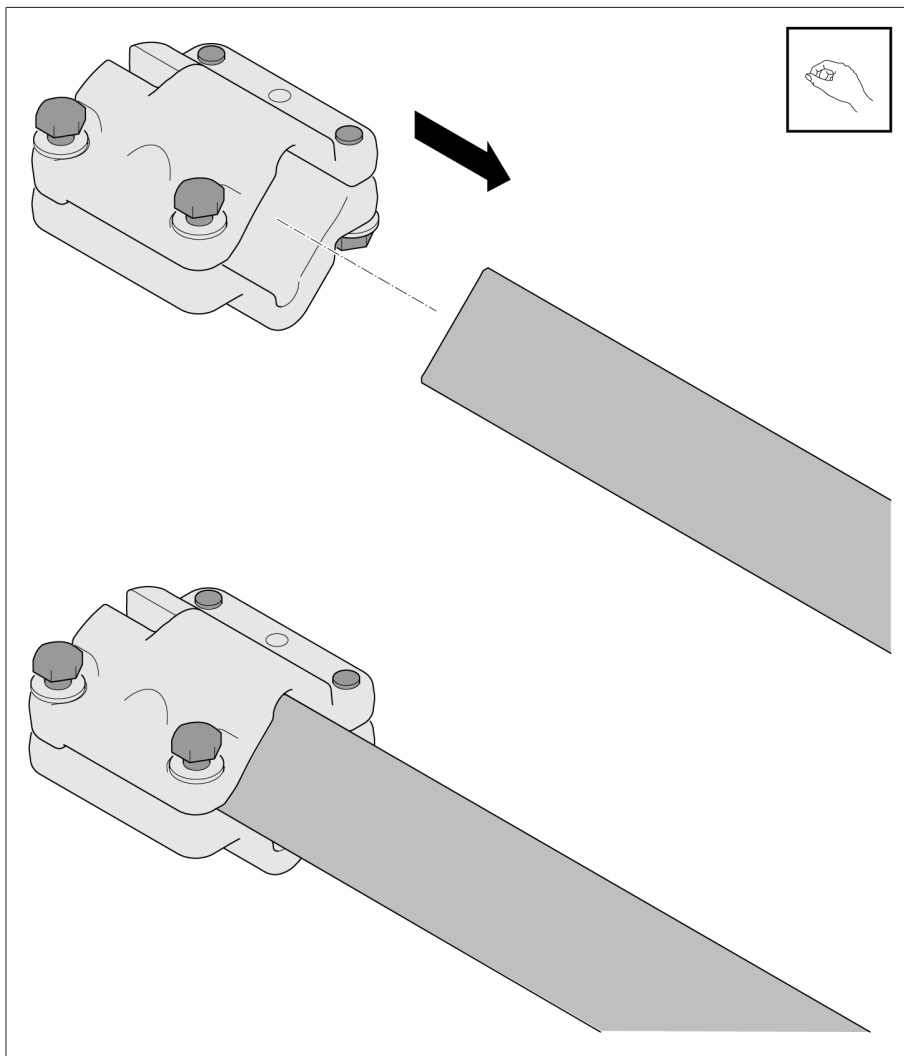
Glisser la pièce d'accouplement sur le tube carré
